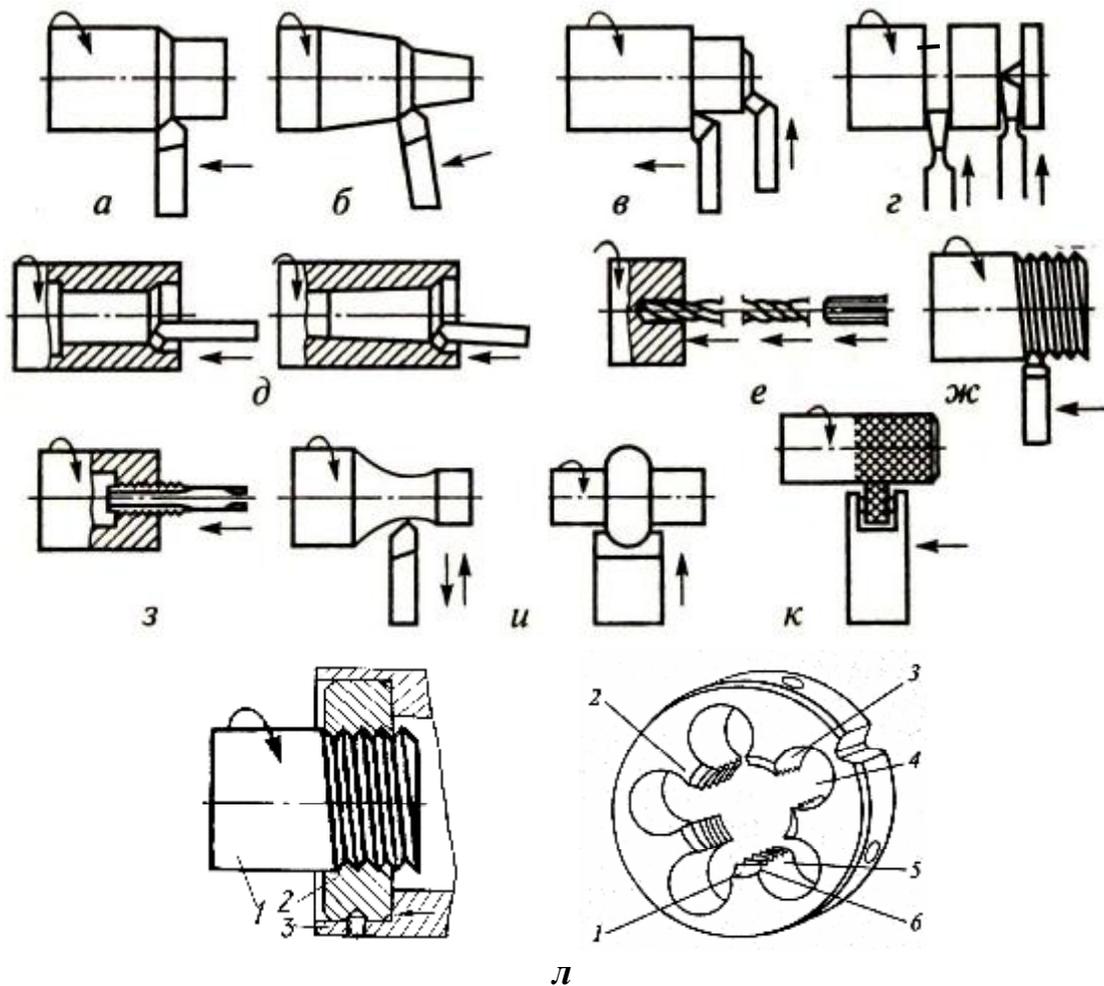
Основные виды токарных работ (стрелками показаны направления перемещения инструмента и заготовки)
